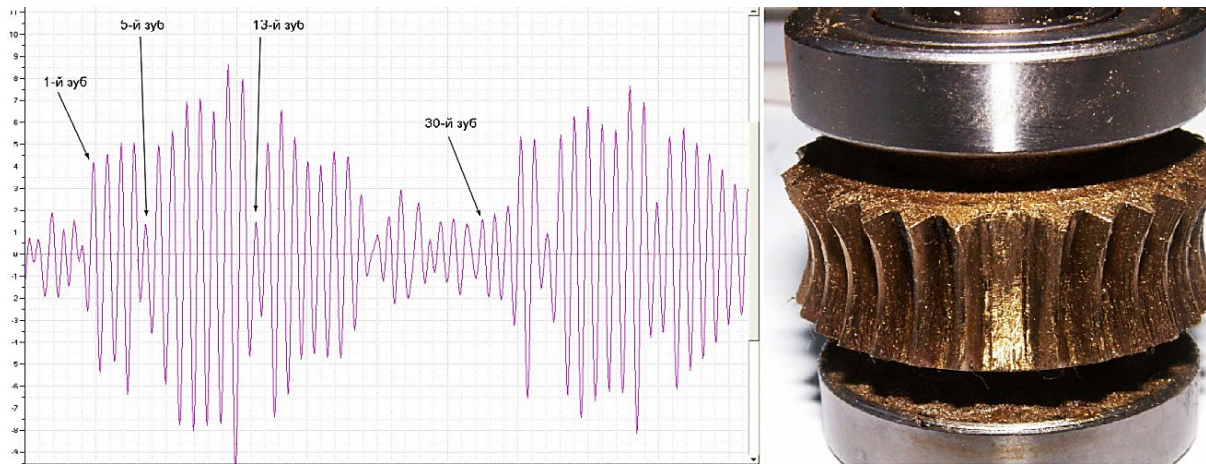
Сигнал дефектного привода (отсутствие зубьев шестерни) [Defective drive signal (missing gear teeth)]
